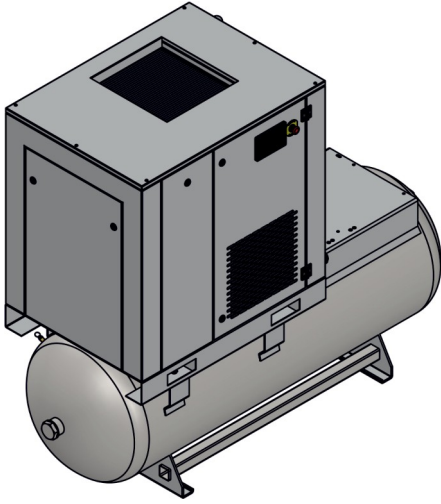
Vedere frontală a compresorului SFTG 11 SXP
